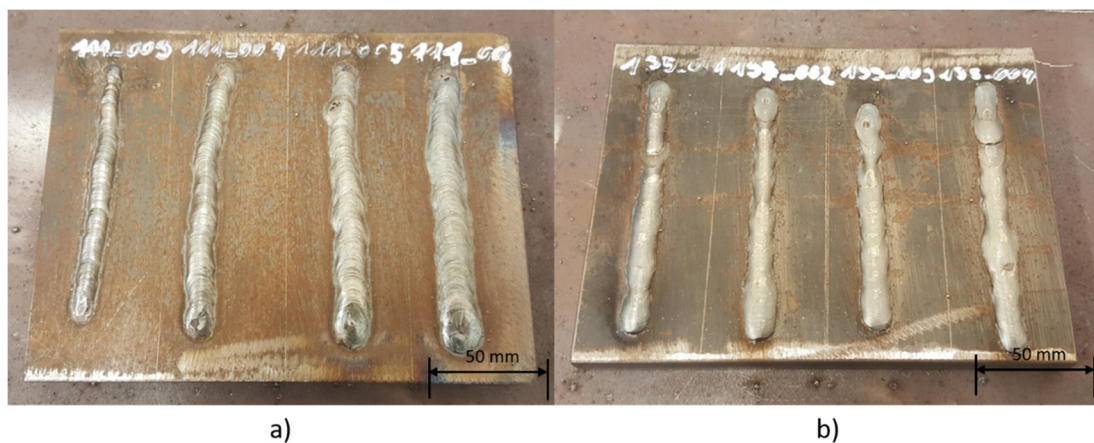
Durchgeführte Auftragsschweißungen a) Elektrodenhandschweißen; b) Metall Aktivgasschweißen
